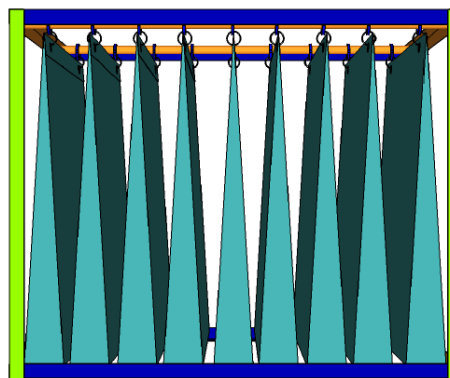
Estrutura metálica com sacos em suspensão. Vista lateral.
